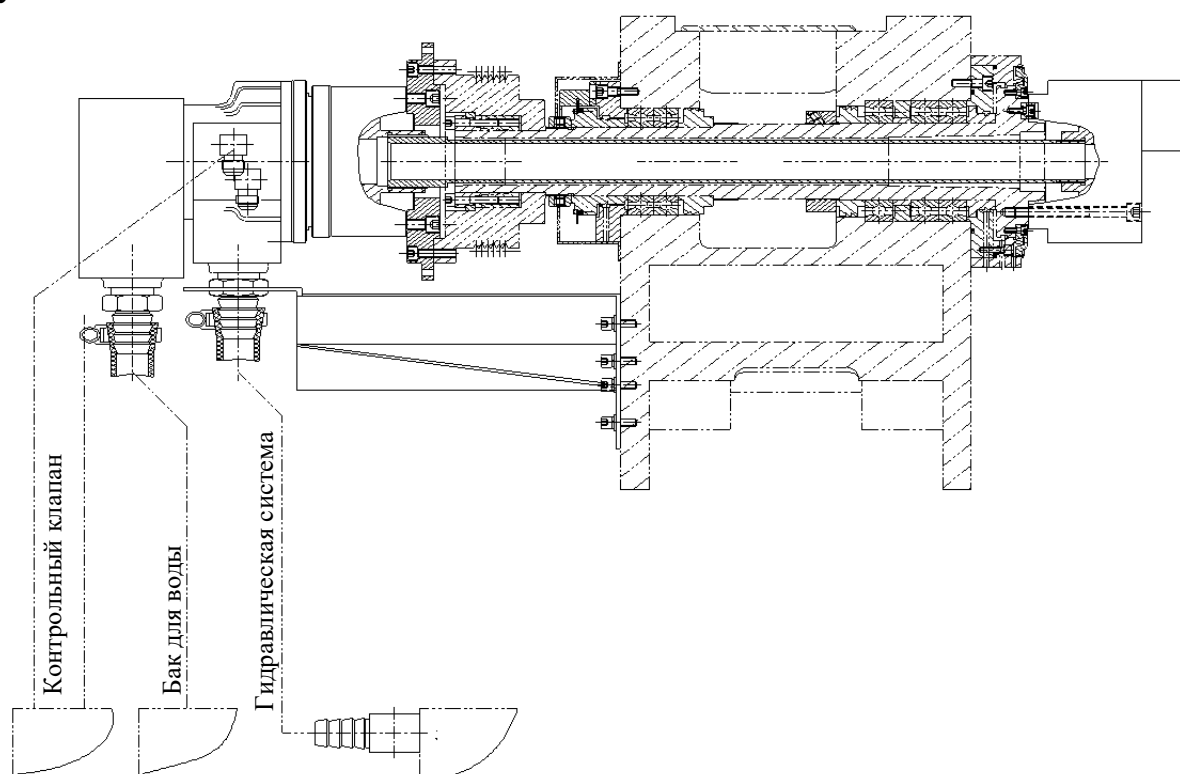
Схема расположения поворотного цилиндра, патрона или приспособления
